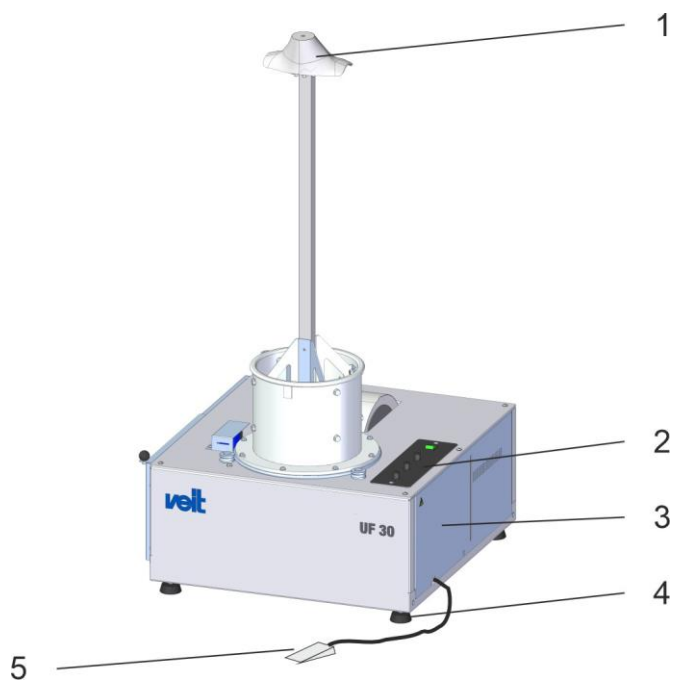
Visão geral da máquina, finalizador universal com busto em jaqueta - UF30 B
